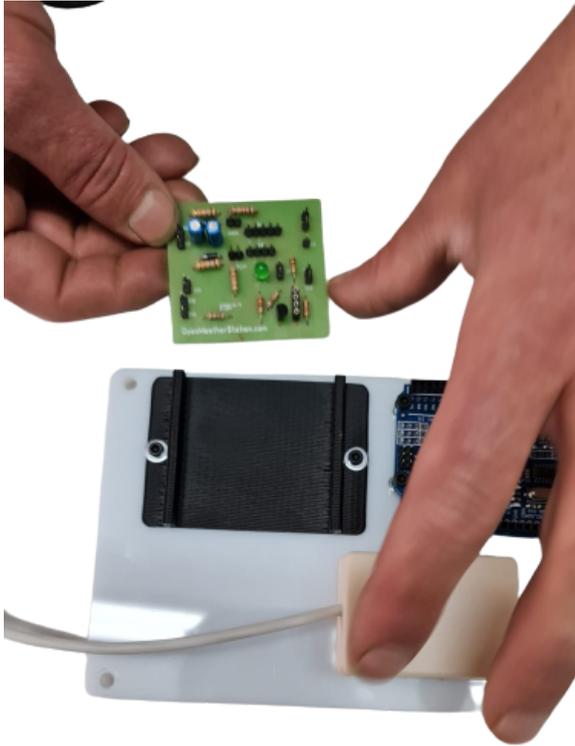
Deslizar la placa PCB sumamente con cuidado a través de las ranuras de la platina de soporte hasta llegar al tope.
